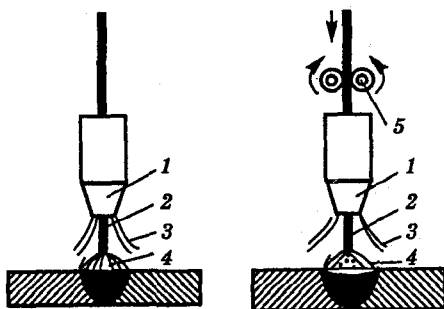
Схемы дуговой сварки в защитных газах:
